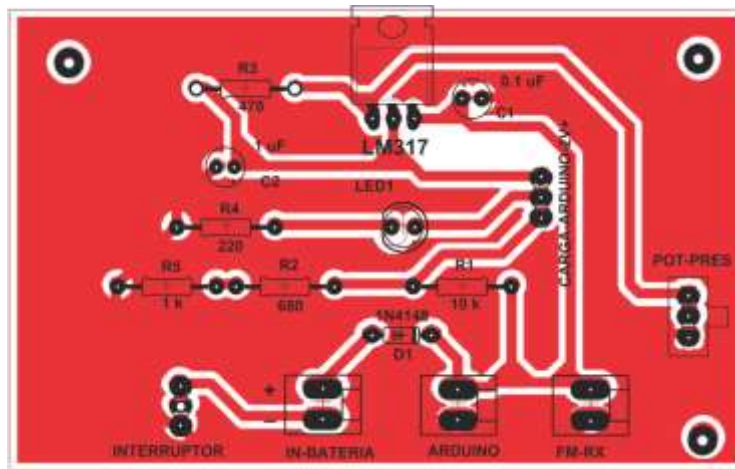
Diseño de la PCB del circuito de alimentación.
